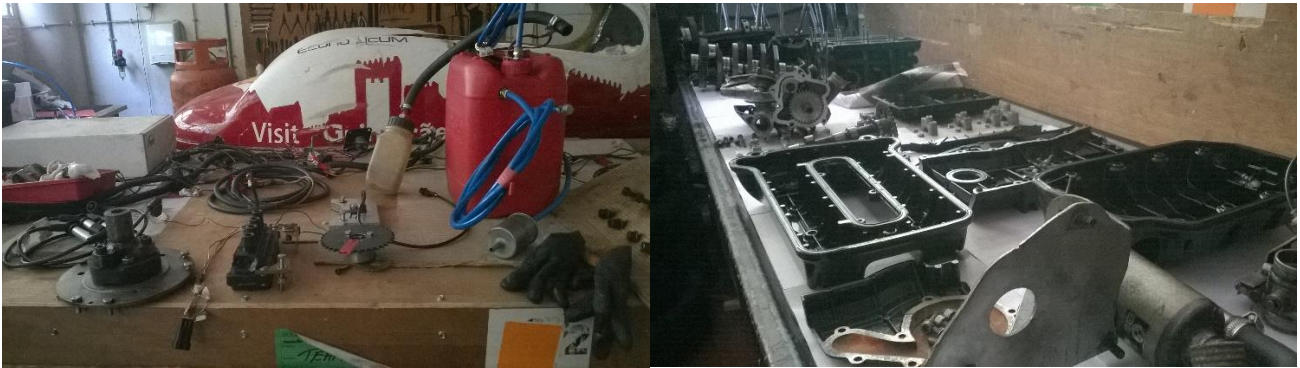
Sistema elétrico (bobine, cablagem, entre outros) e sistema de combustível (à esquerda); Motor BMW K75 em peças (à direita)
